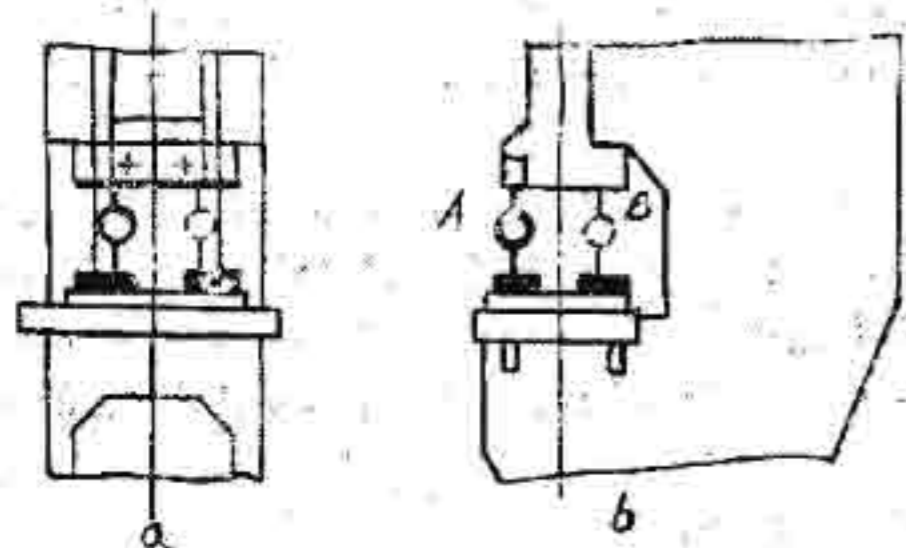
检验滑块下平面对工作台板上平面的平行度
